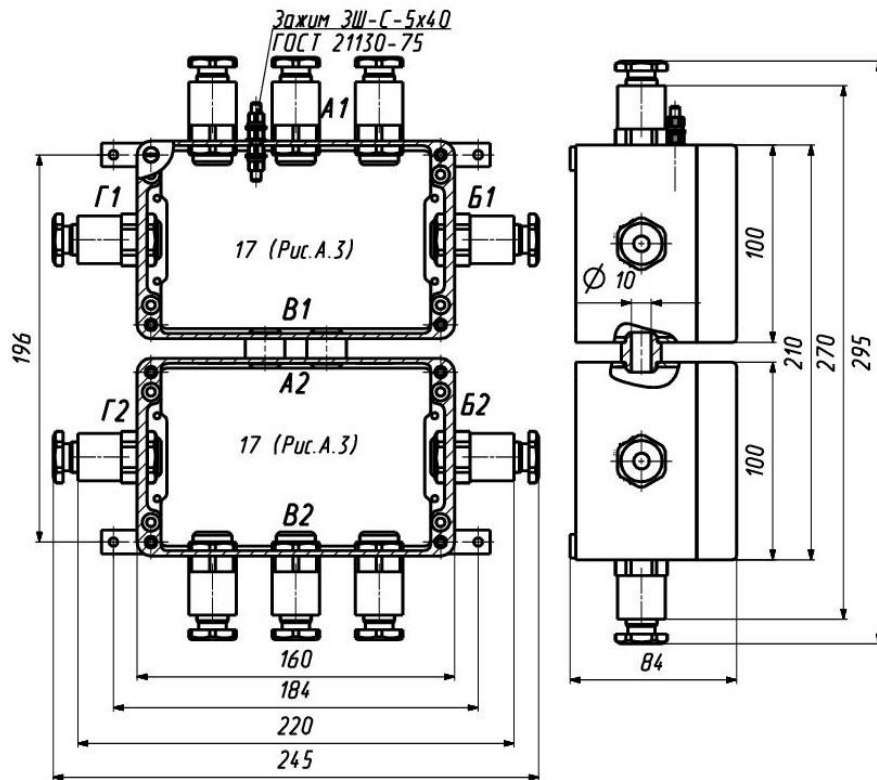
Блок корпусов и коробка клеммная ЕхБКО-А17В1/А17А2 (скрепление двух корпусов типоразмера 17 сторонами В1 и А2) – вариант 3
